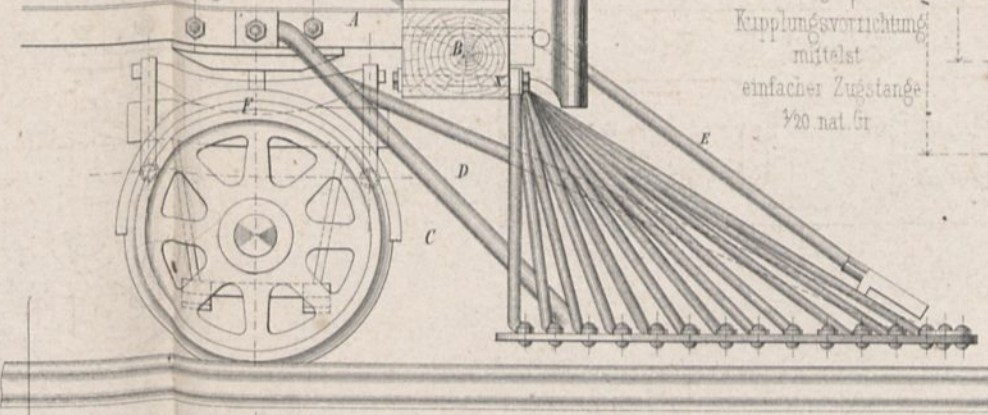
Grundriss Amerikanisches Räumergestell
